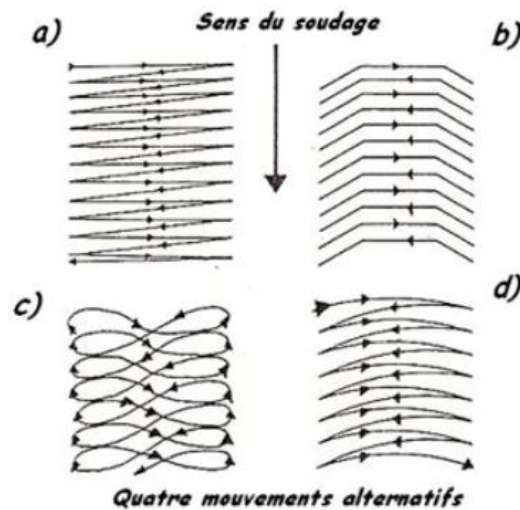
Les mouvements alternatifs de soudage [22]
